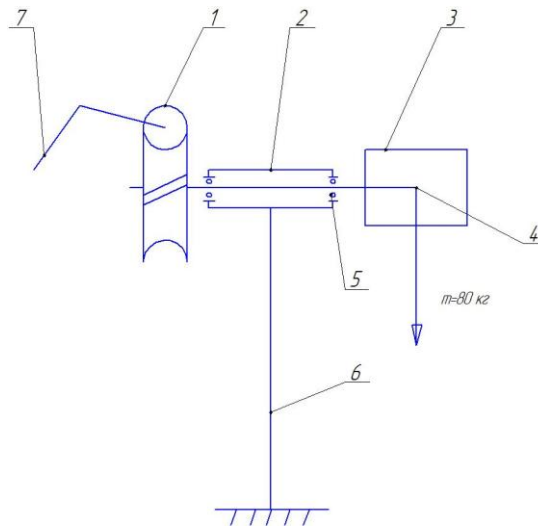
Кинематическая схема стенда: 1-червячный редуктор, регулировочного рычага тормозов Зил-130, 2-корпус, 3-обслуживаемый задний мост, 4-станина, 5-подшипник, 6-стойка, 7-ручка редуктора
